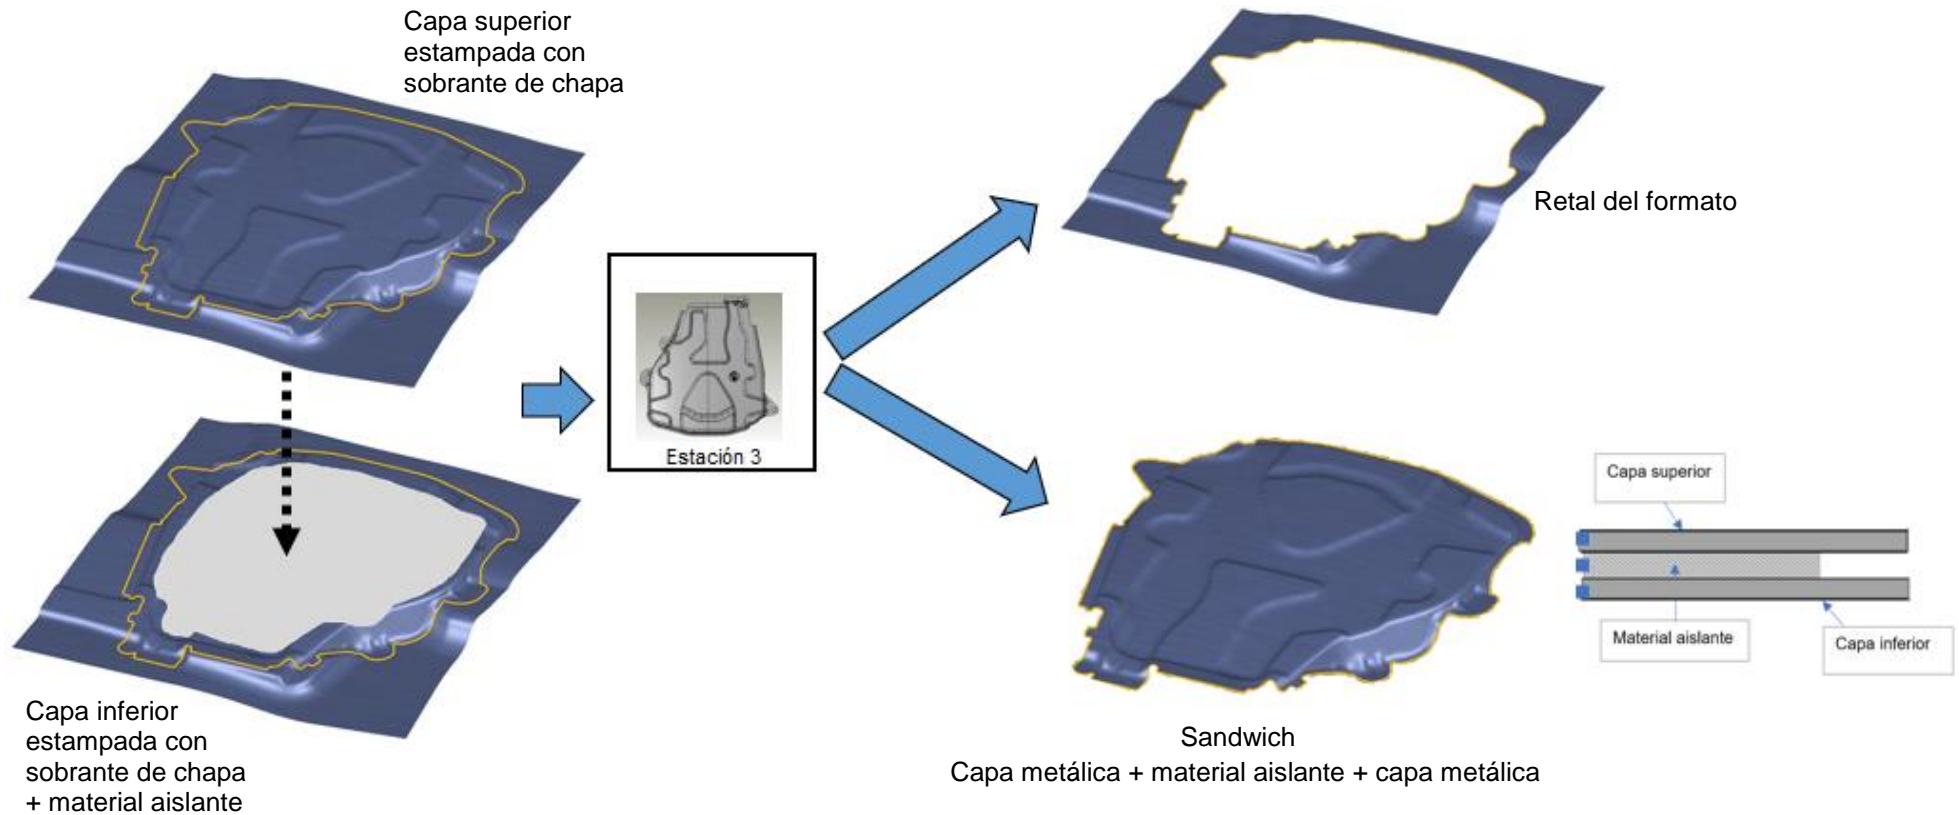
Diagrama estación 3 - sandwich + corte perimetral
